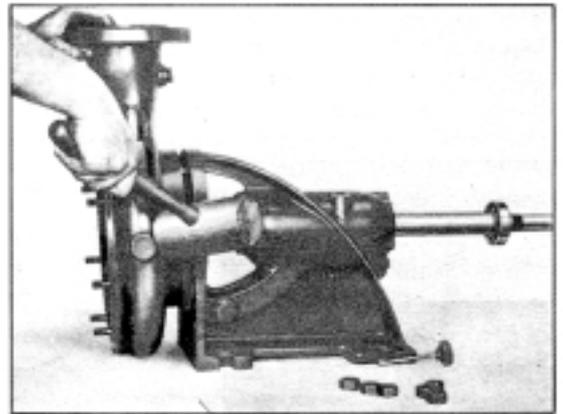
Desmontaje del cuerpo del caballete de los rodamientos
